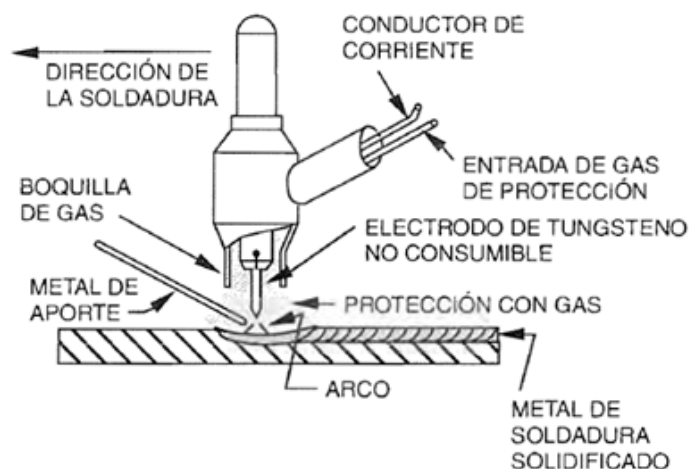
Proceso de soldadura GTAW [3]
